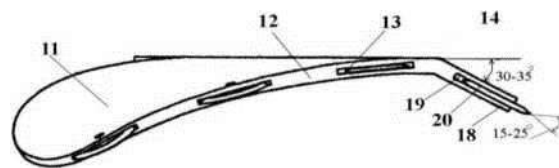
Лопасть-нож смесителя (вид сверху): 11 - лопасть; 12 - верхняя поверхность лопасти; 13,19 - паз; 14,20 - нож; 18 - передняя поверхность лопасти
